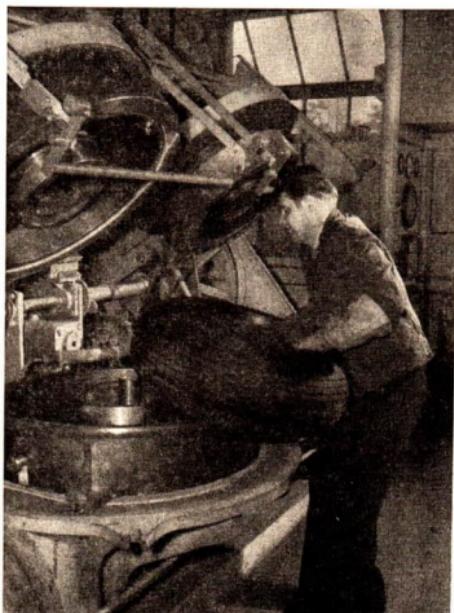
Reifen für Flugzeuge und Fahrzeuge
